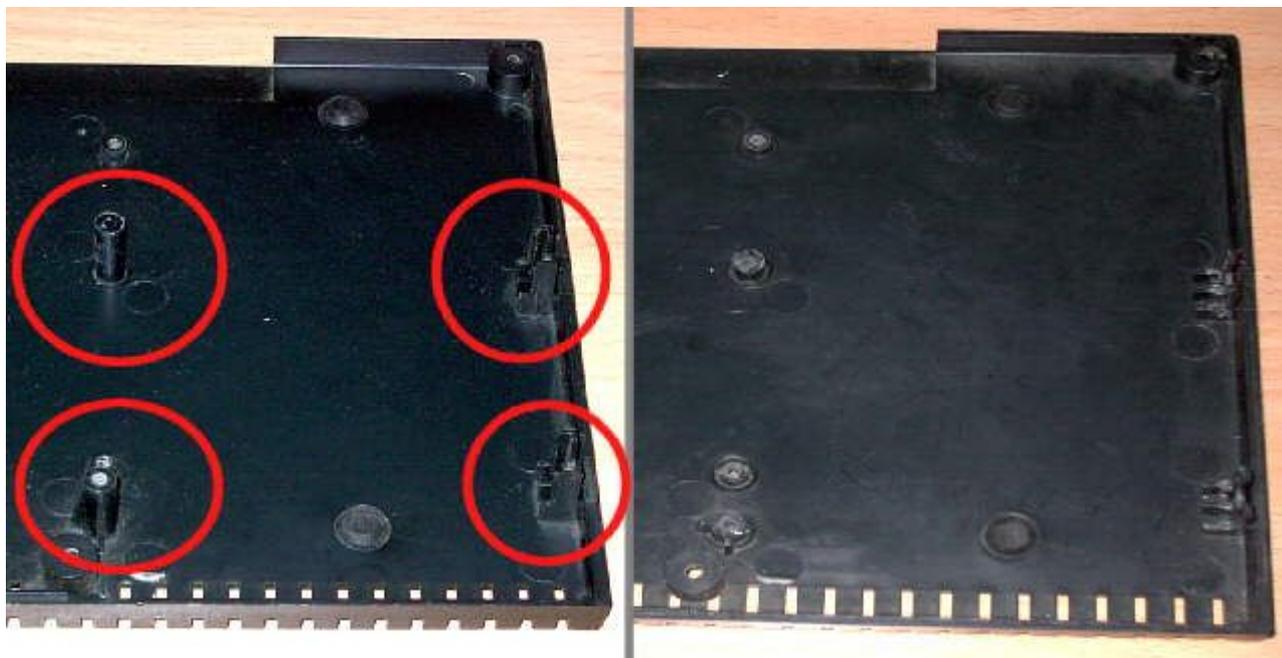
Parte inferior de la carcasa antes (izquierda) y después (derecha)
